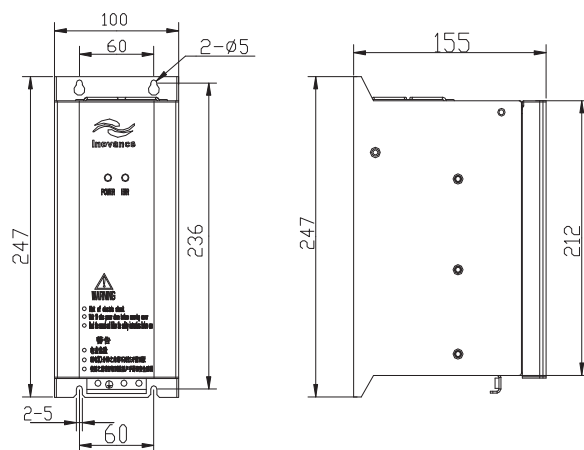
MDBU-70-X外形尺寸及安装尺寸示意图
